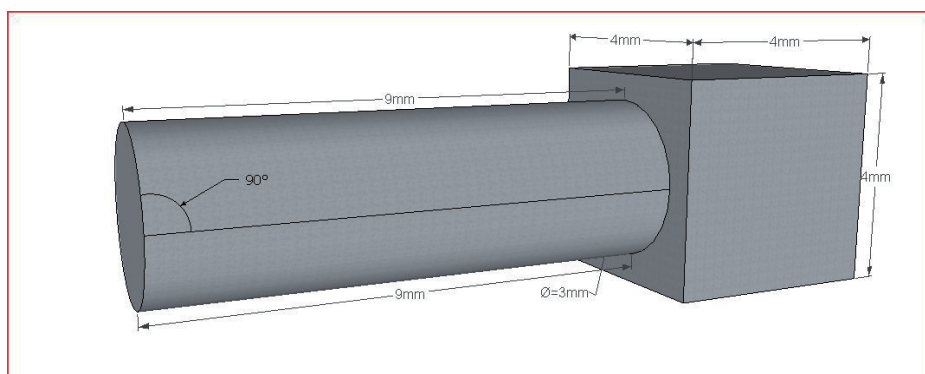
Hemicorpo de prova para posterior soldagem na vertical 90° (grupo C90 e T90).
